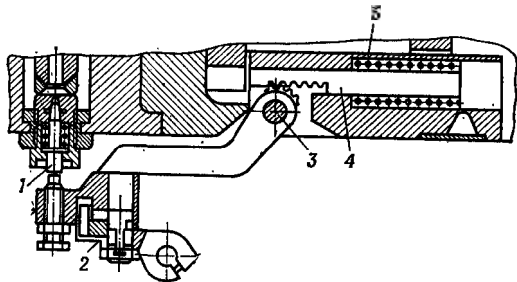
Схема устройства орудийного ударного механизма молоткового типа: 1 — боек; 2 — молоток; 3 — ось; 4 — поршень с рейкой; 5 — боевая пружина.
